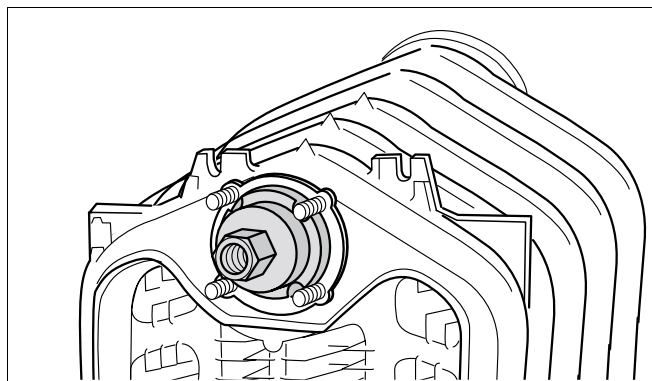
Montarea utilajului de presare pentru elementul frontal.
